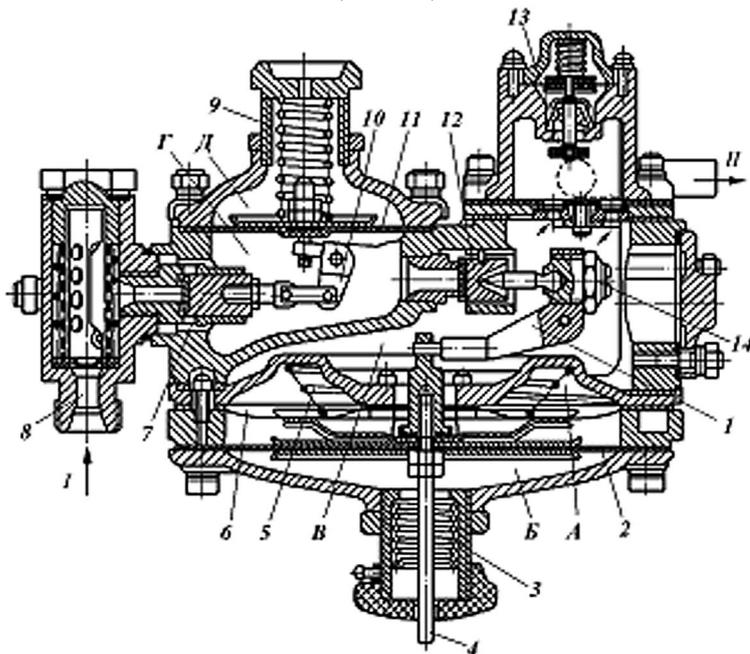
Двухступенчатый газовый редуктор низкого давления
